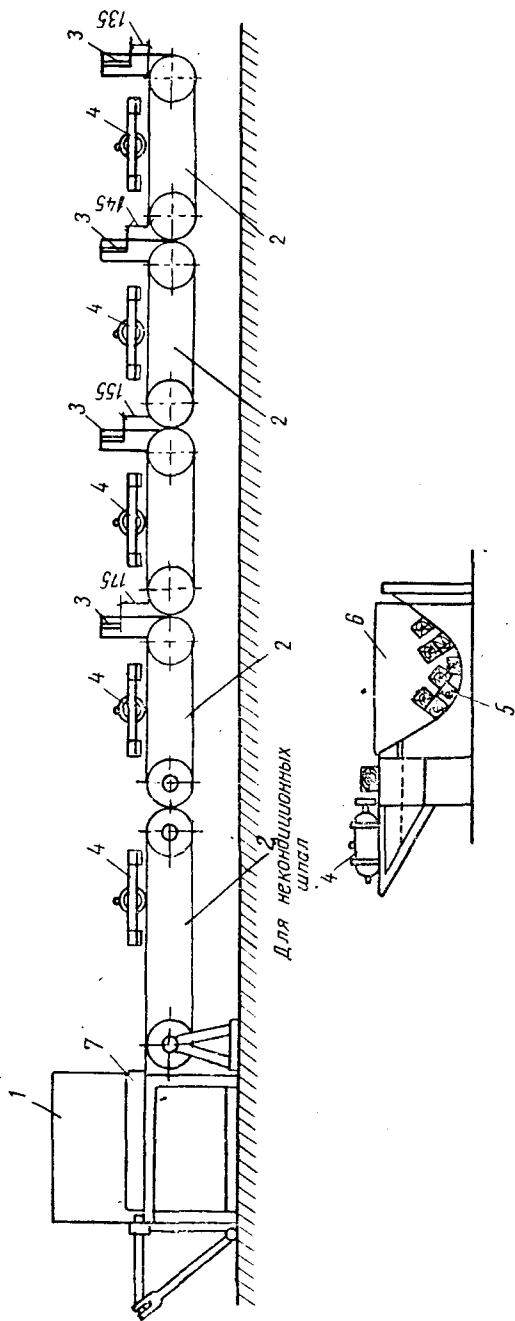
Схема механизма для рассортировки шпал по типам (по толщине):
